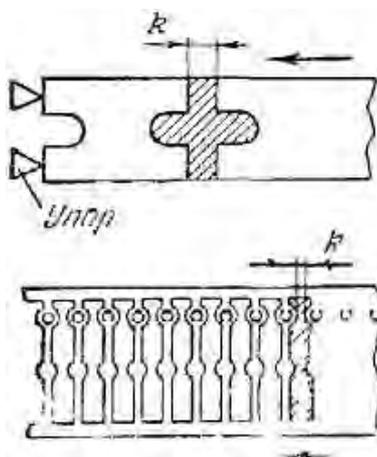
Получение заготовки путем вырубки перемычки (в виде отхода)
